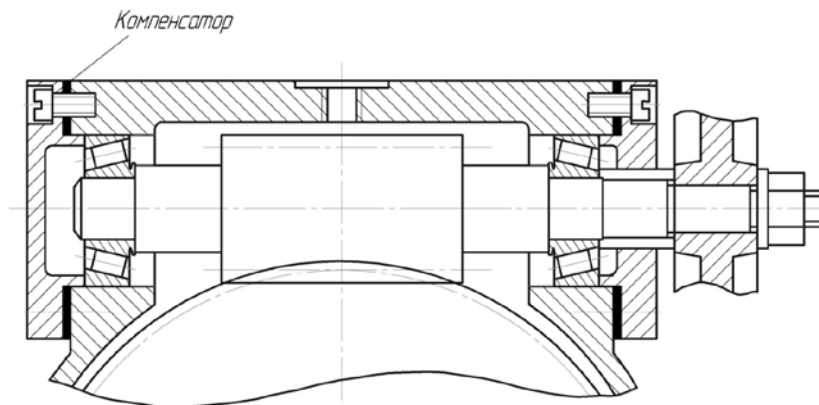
Способ регулировки осевого зазора в коническом роликовом подшипнике
